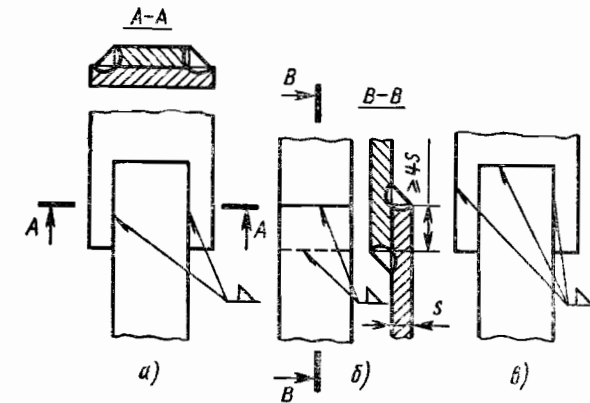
Нахлесточные соединения, выполненные: а — фланговыми швами; б — лобовыми швами; в — комбинированным (фланговыми и лобовым) швом
